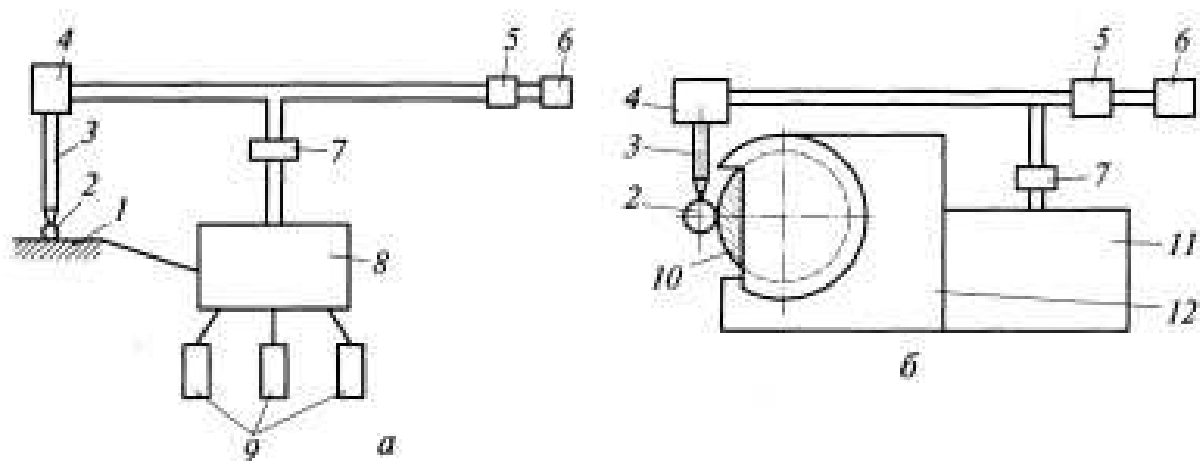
Схемы автоматов пассивного {а) и активного {б) контроля: 1 — измерительное приспособление; 2 — деталь; 3 — шток; 4 — размерный датчик; 5 — счетчик; 6 — сигнализация; 7 — промежуточное звено; 8 — сортировочное устройство; 9 — ящик для рассортирования деталей; 10 — инструмент; 11 — исполнительный механизм; 12 — шлифовальная бабка
